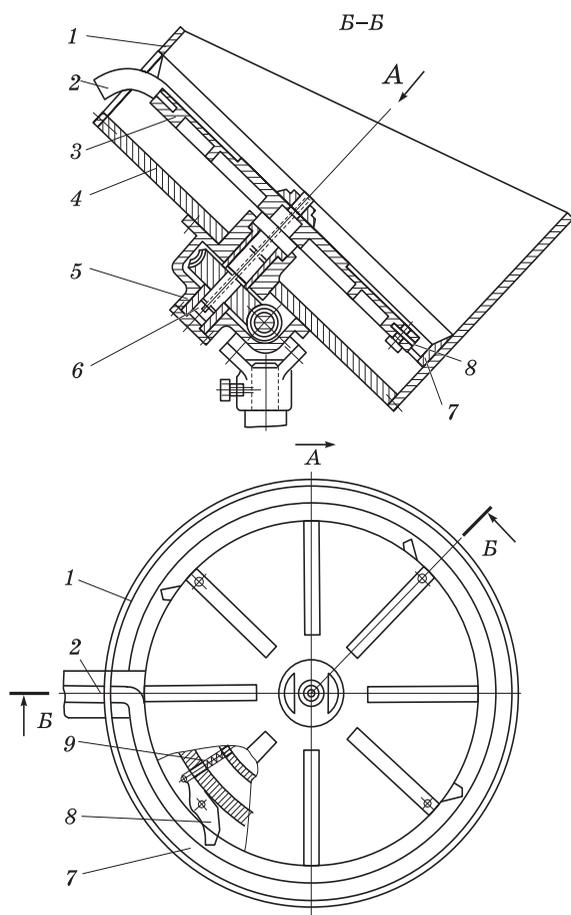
Схема щелевого бункерного устройства для метизов
